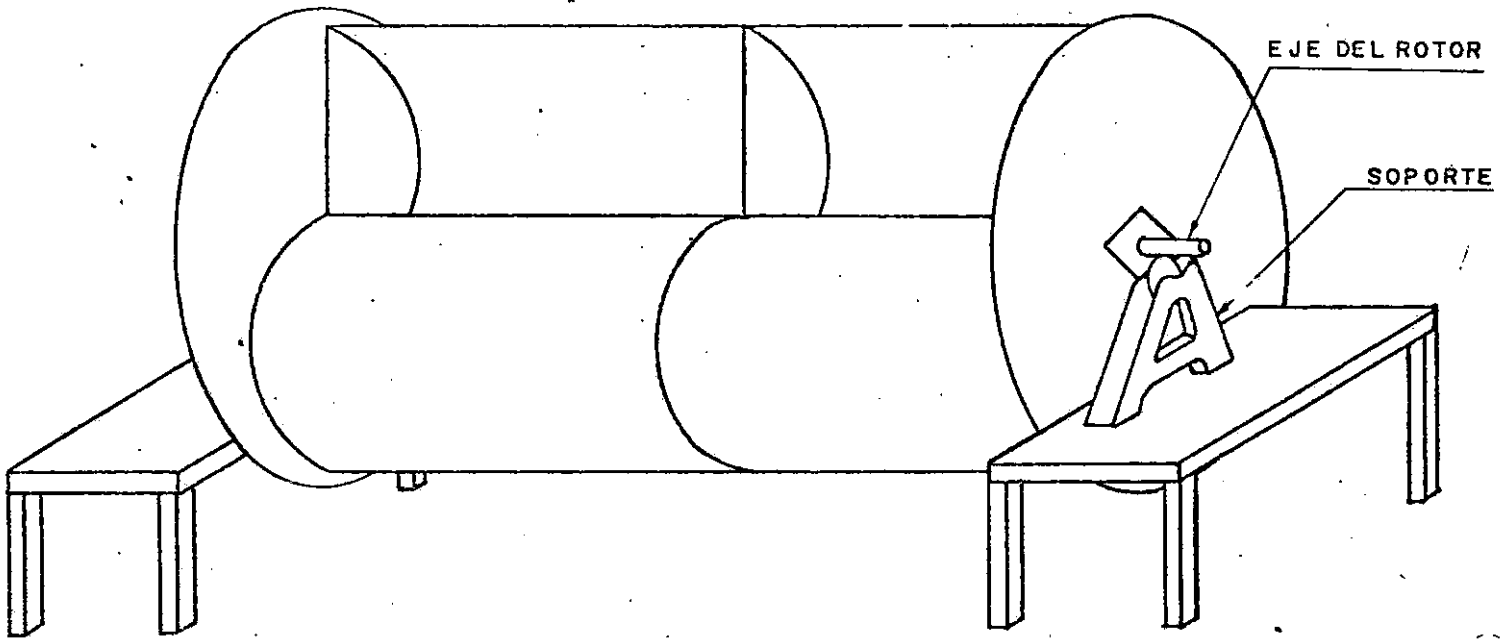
POSICION HORIZONTAL DEL ROTOR SOBRE DOS SOPORTES PARA SU BALANCEO Y AJUSTE
